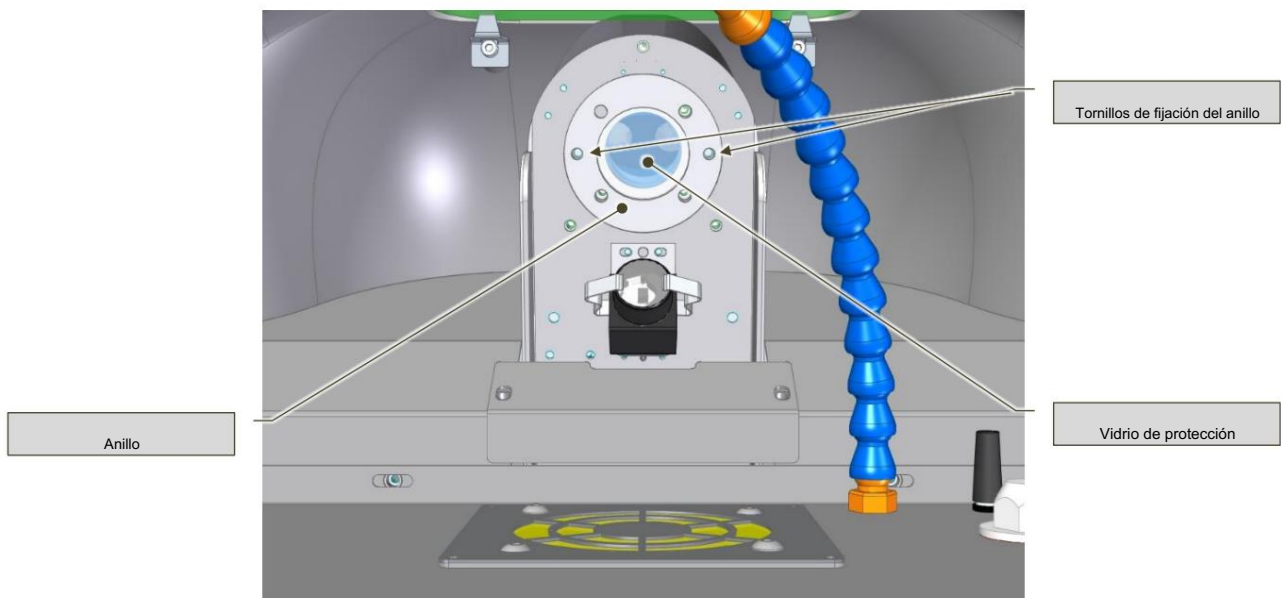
Sustitución del cristal de protección especial – vista desde abajo de la cámara de soldadura
